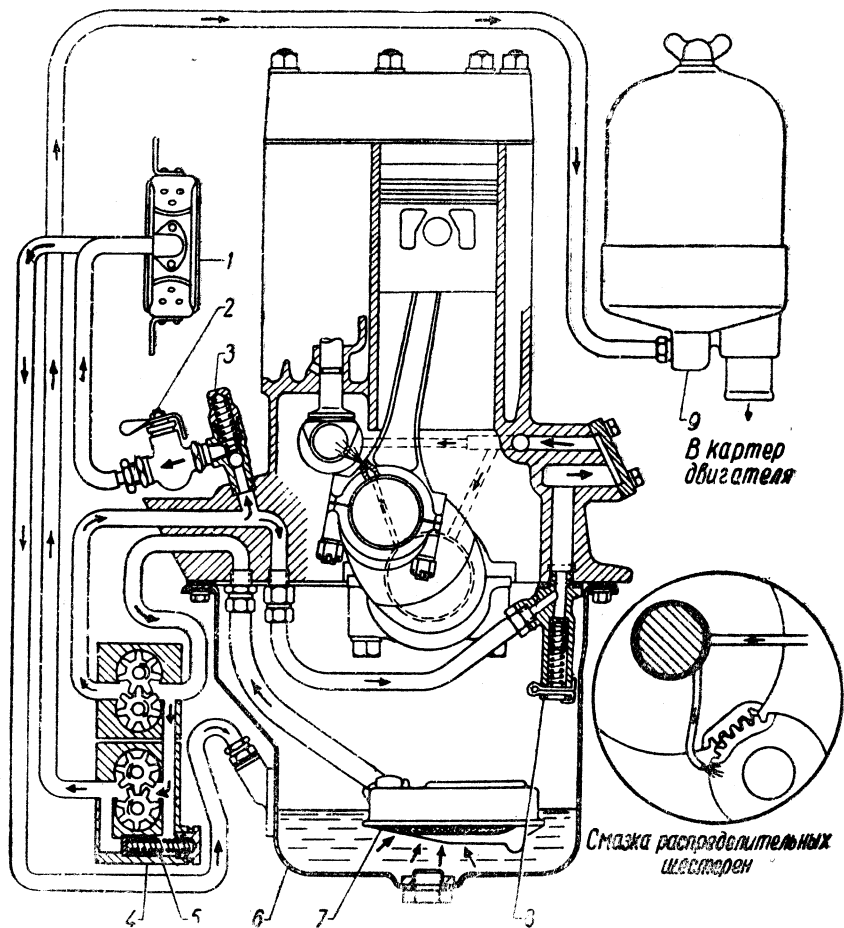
Схема смазки двигателя с центробежным фильтром.
